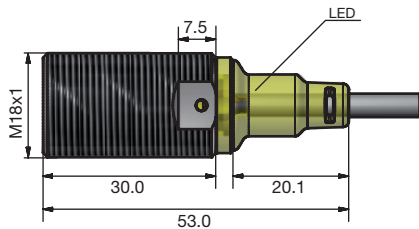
Kurze Ausführung, bündiger Einbau, Kabel
